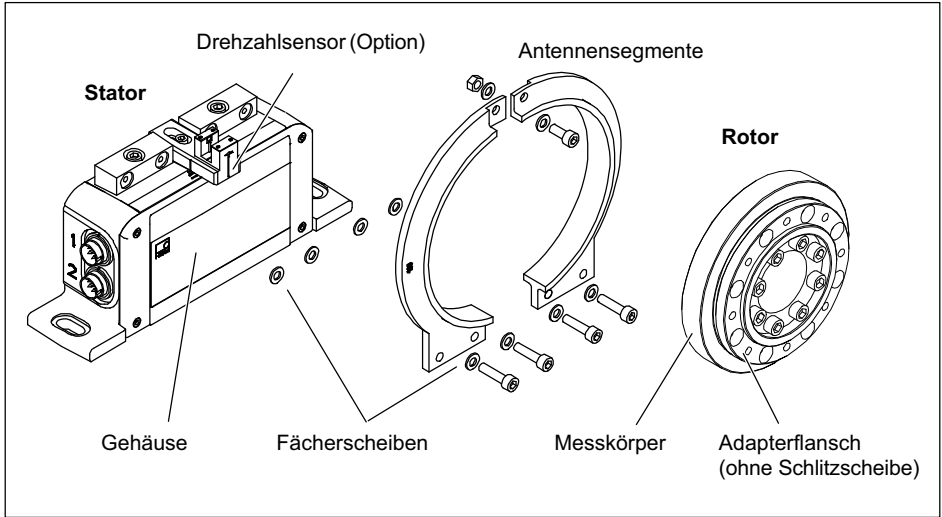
Mechanischer Aufbau, Explosionsdarstellung
